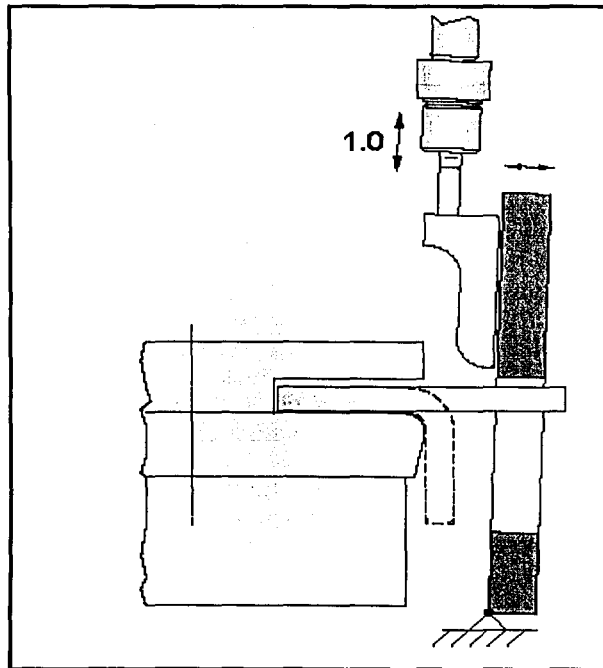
Plano de situación para el dispositivo plegador.
